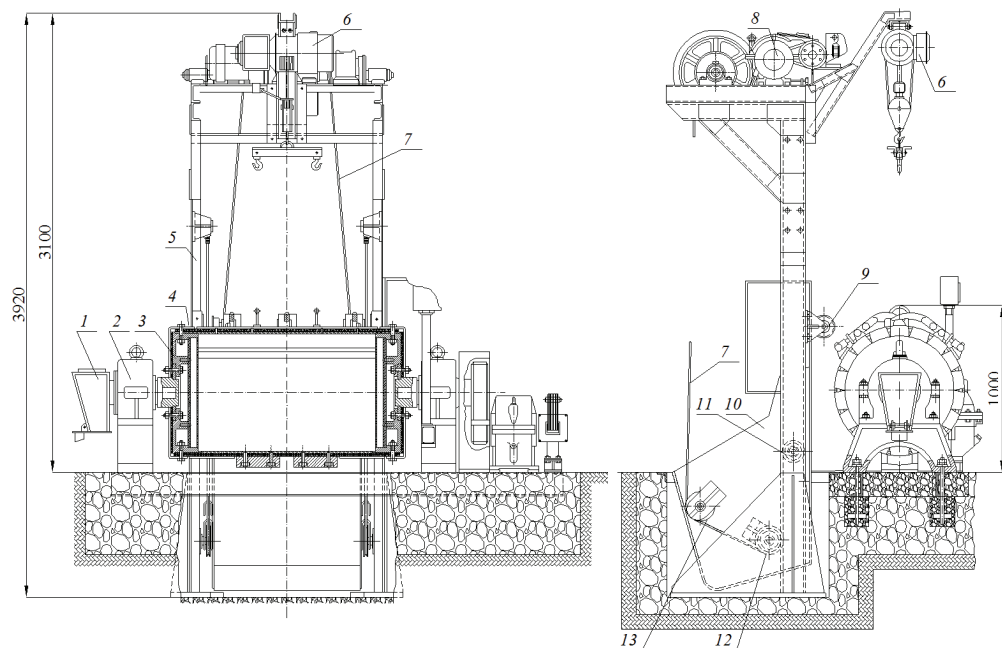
Устройство галтовочного периодического действия модели ОБ-800: 1 – патрубок вытяжной; 2 – опора цапф барабана; 3 – барабан; 4 – крышка барабана; 5 – направляющая цапфа; 6 – электротельфер; 7 – трос скипа; 8 – привод скипового подъемника; 9 – шкив направляющий; 10 – ковш скипового подъемника; 11, 12 – каток ковша; 13 – блок
